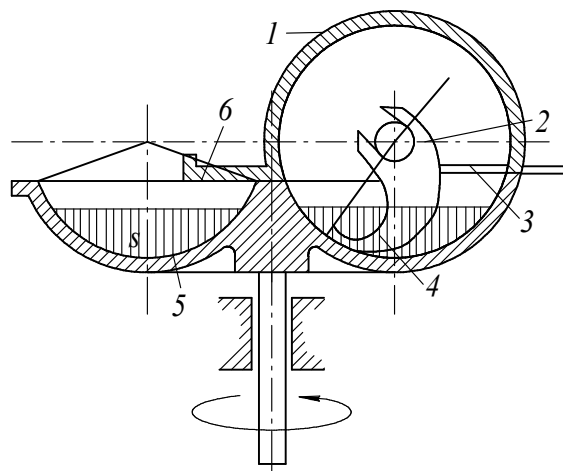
Схема роботи кутера періодичної дії: 1 - кришка; 2 - вал; 3 - гребінка; 4 - ножі; 5 - чаша; 6 - скребок
